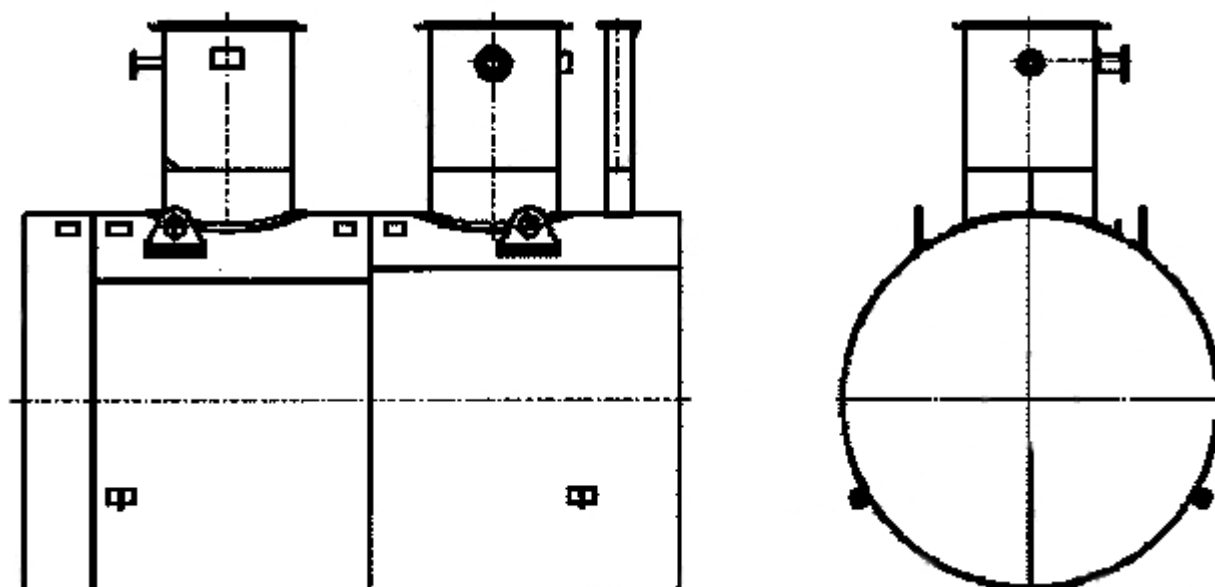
Общий вид резервуаров ЕП-16-2000-1424-1
